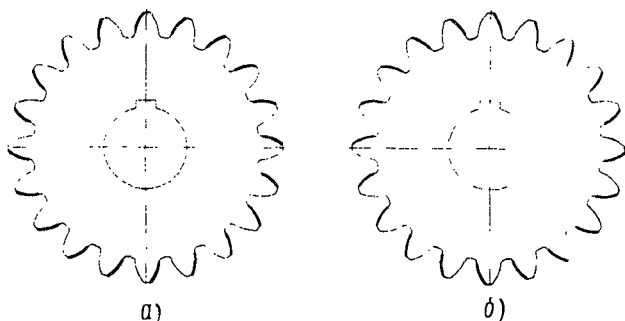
Рабочие МП зубчатого венца шестерни:
